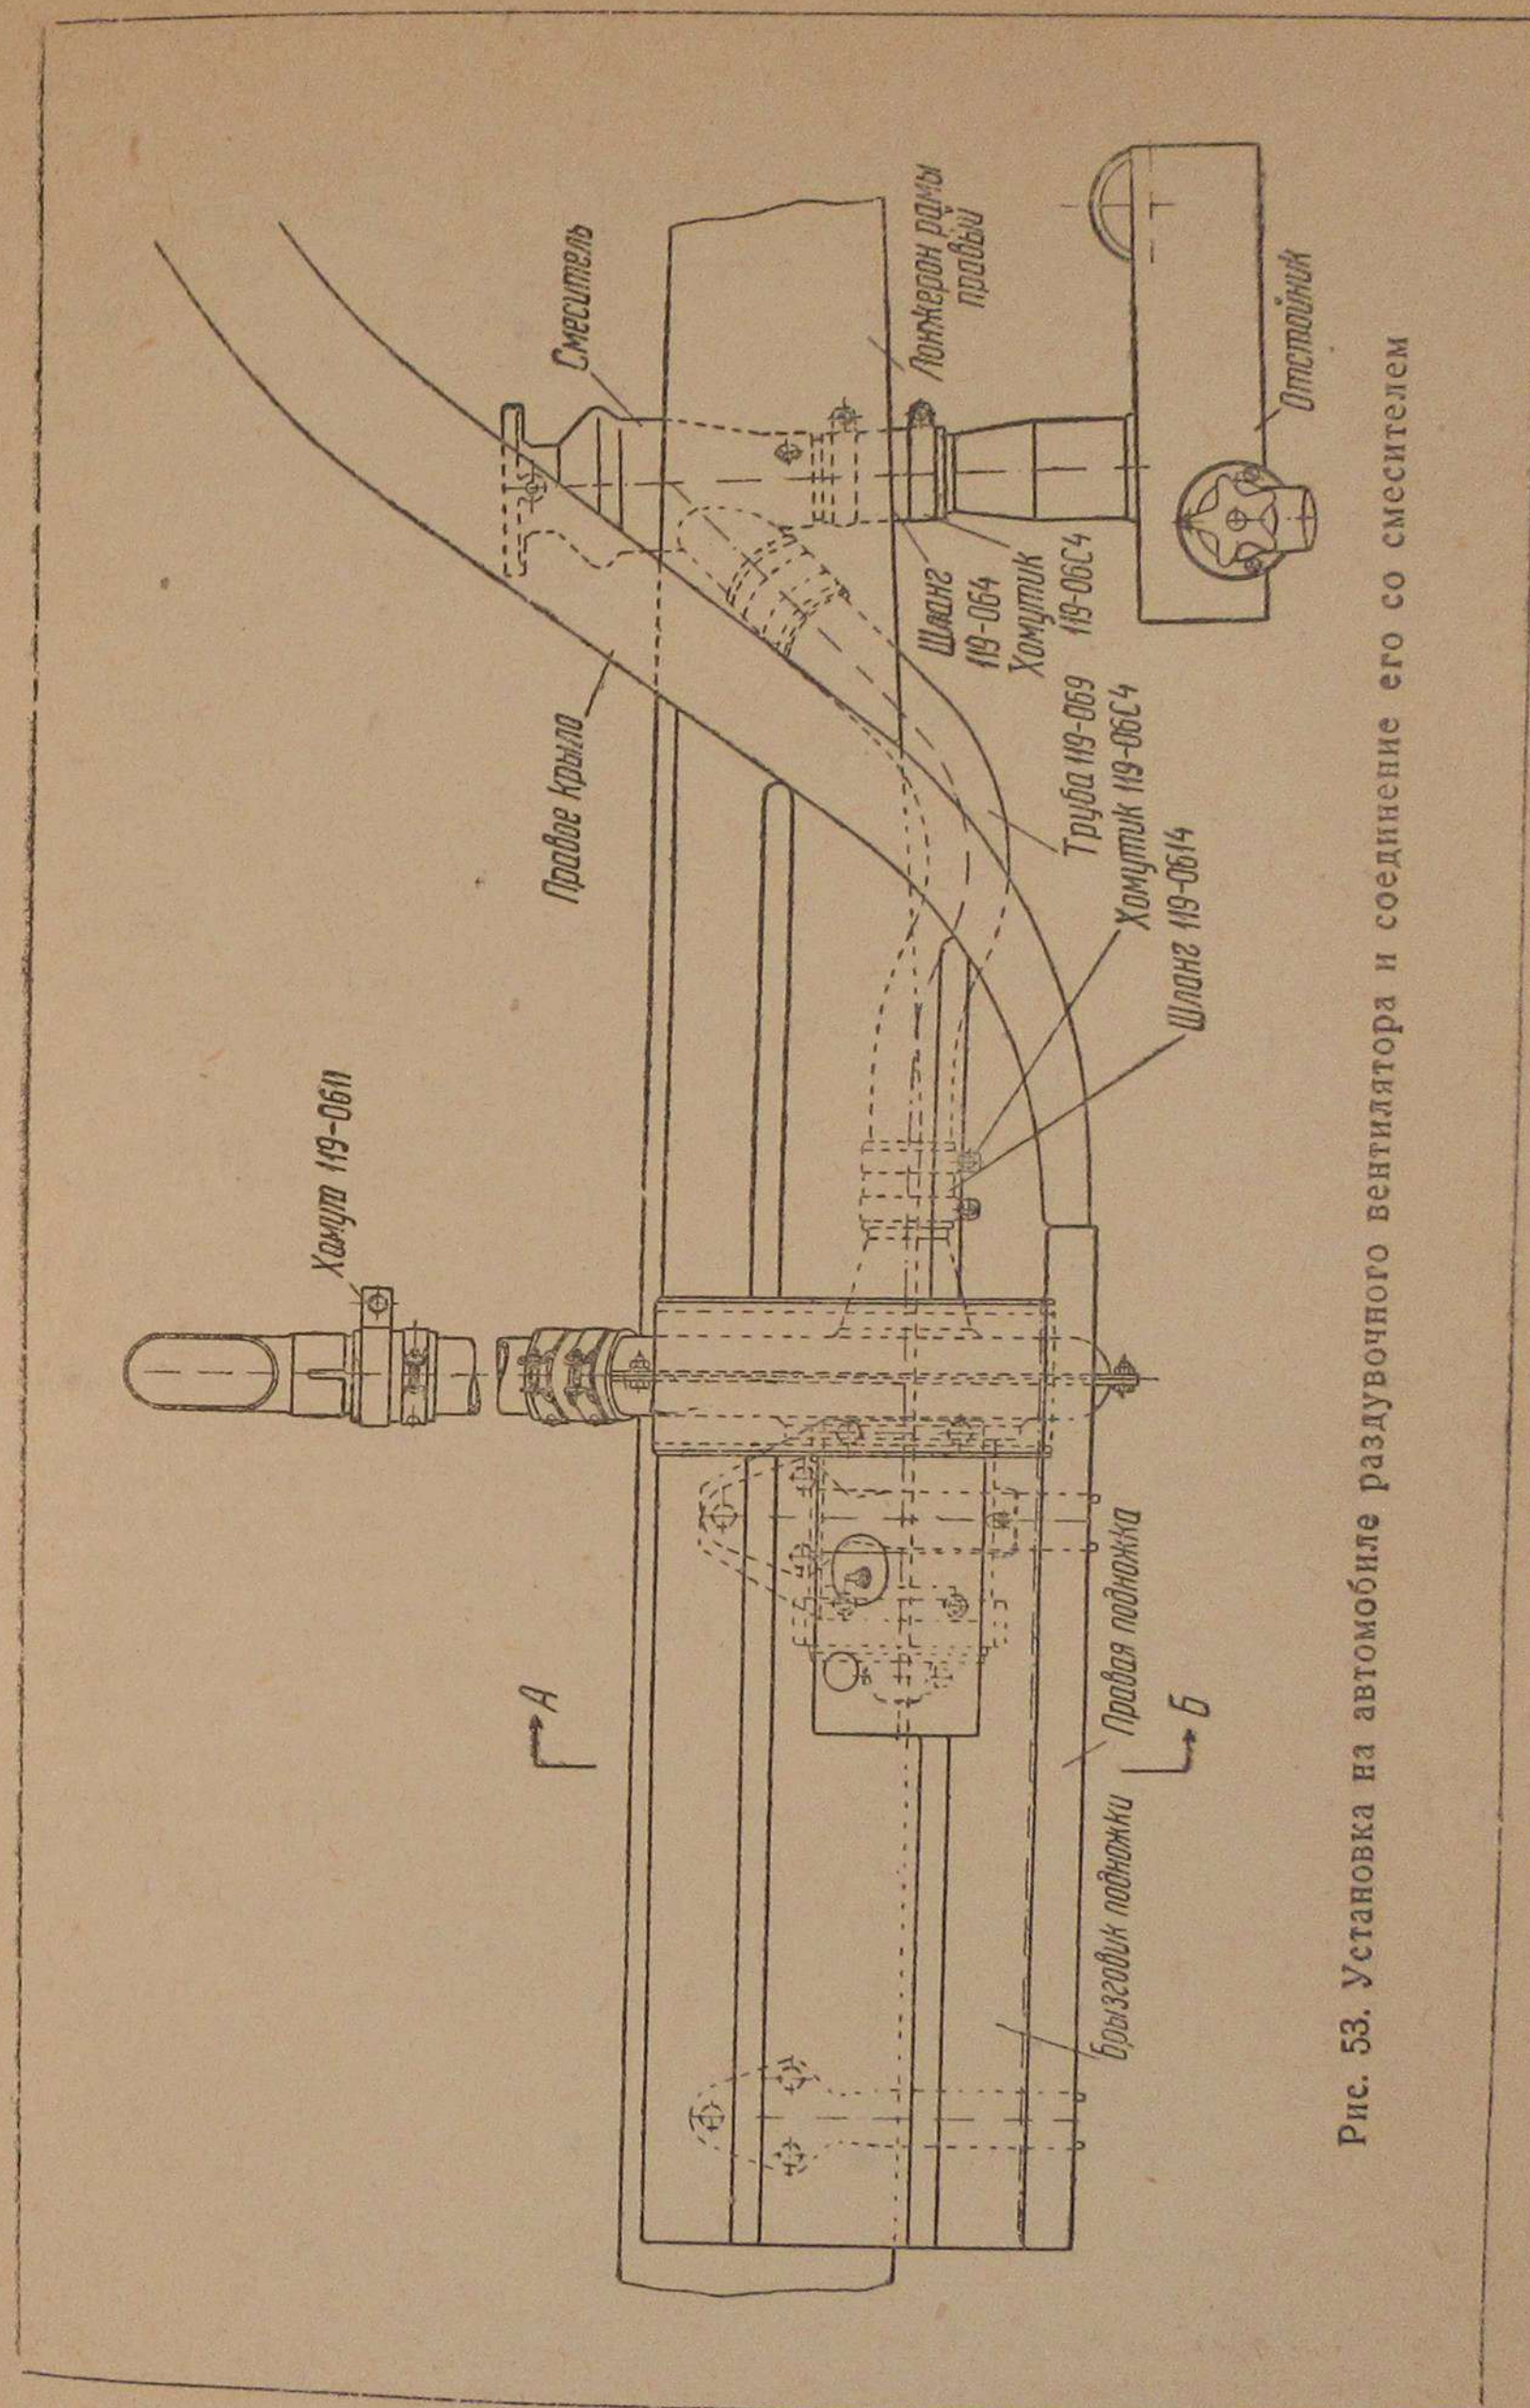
Установка на автомобиле раздувочного вентилятора и соединение его со смесителем
